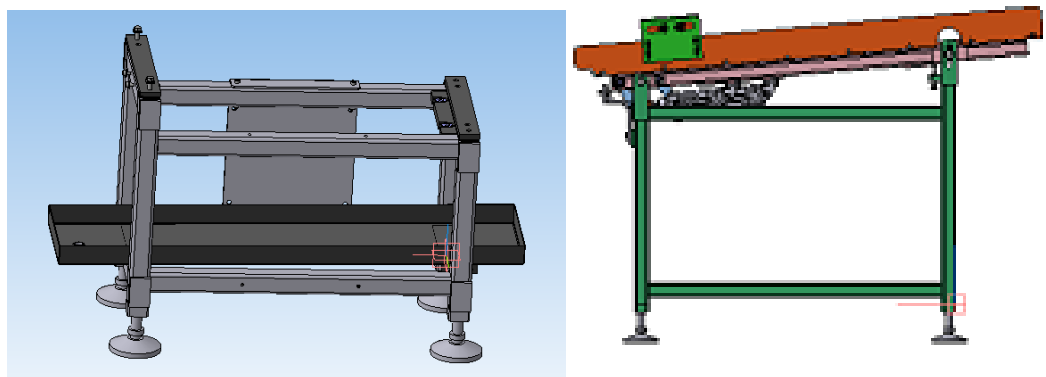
Загальний вигляд завантажувача і накопичувача заготовок
